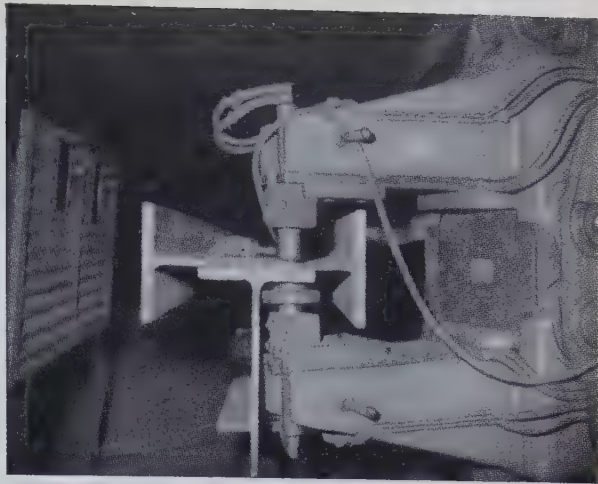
Die Schweißarme der Maschine während des Schweißvorganges
